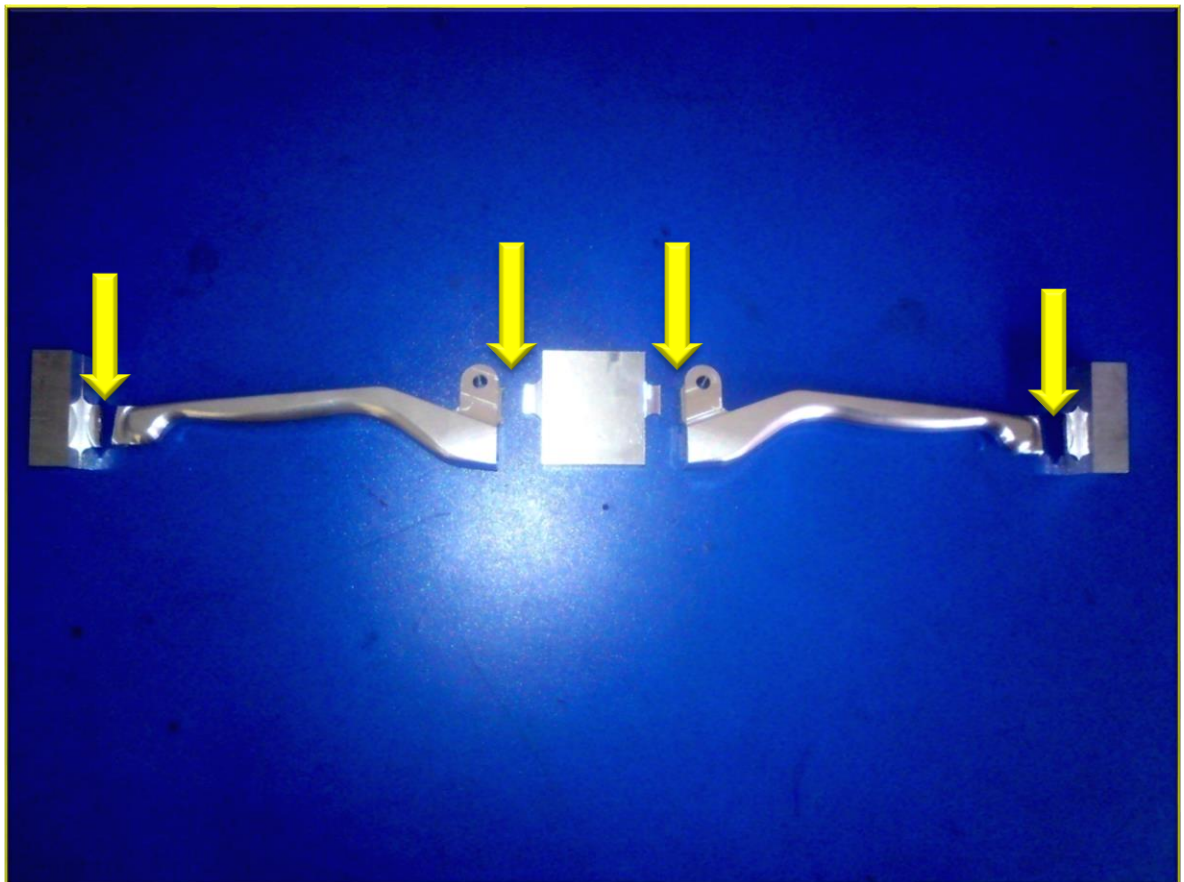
Obrobek po příkazu „řádkování“ ve druhém upnutí
